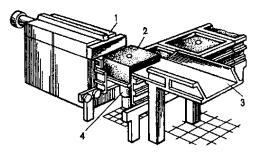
Автоматическая установка для выбивки отливок из форм: 1 – толкатель, 2 – форма, 3 – виброжелоб, 4 – гидравлический выталкиватель
